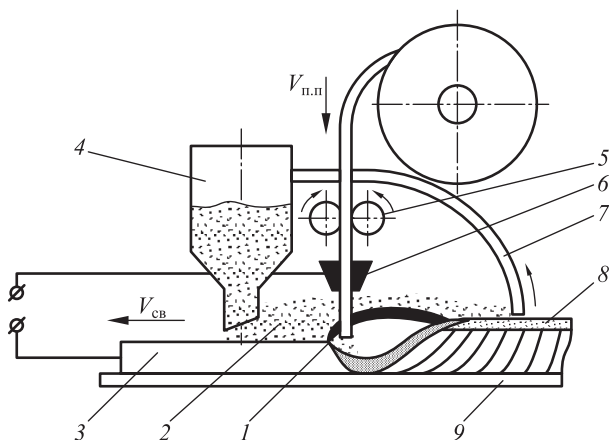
Схема автоматической сварки под флюсом:
